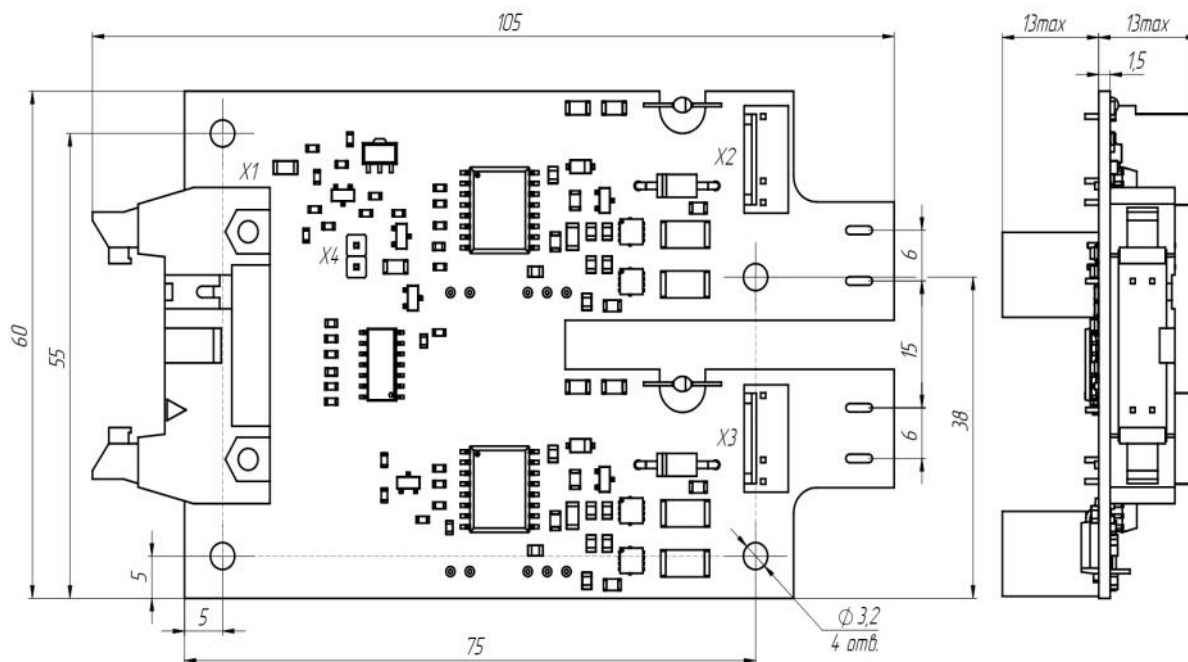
Чертеж драйвера DI28-17-E-1
